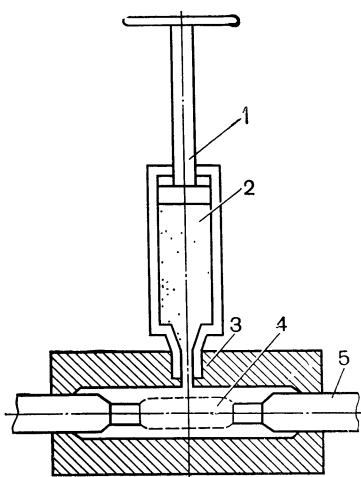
Опрессование сrostка расплавленным полиэтиленом: 1 — ручной пресс; 2 — расплавленный полиэтилен; 3 — пресс-форма; 4 — сrostок сердечника; 5 — кабель
